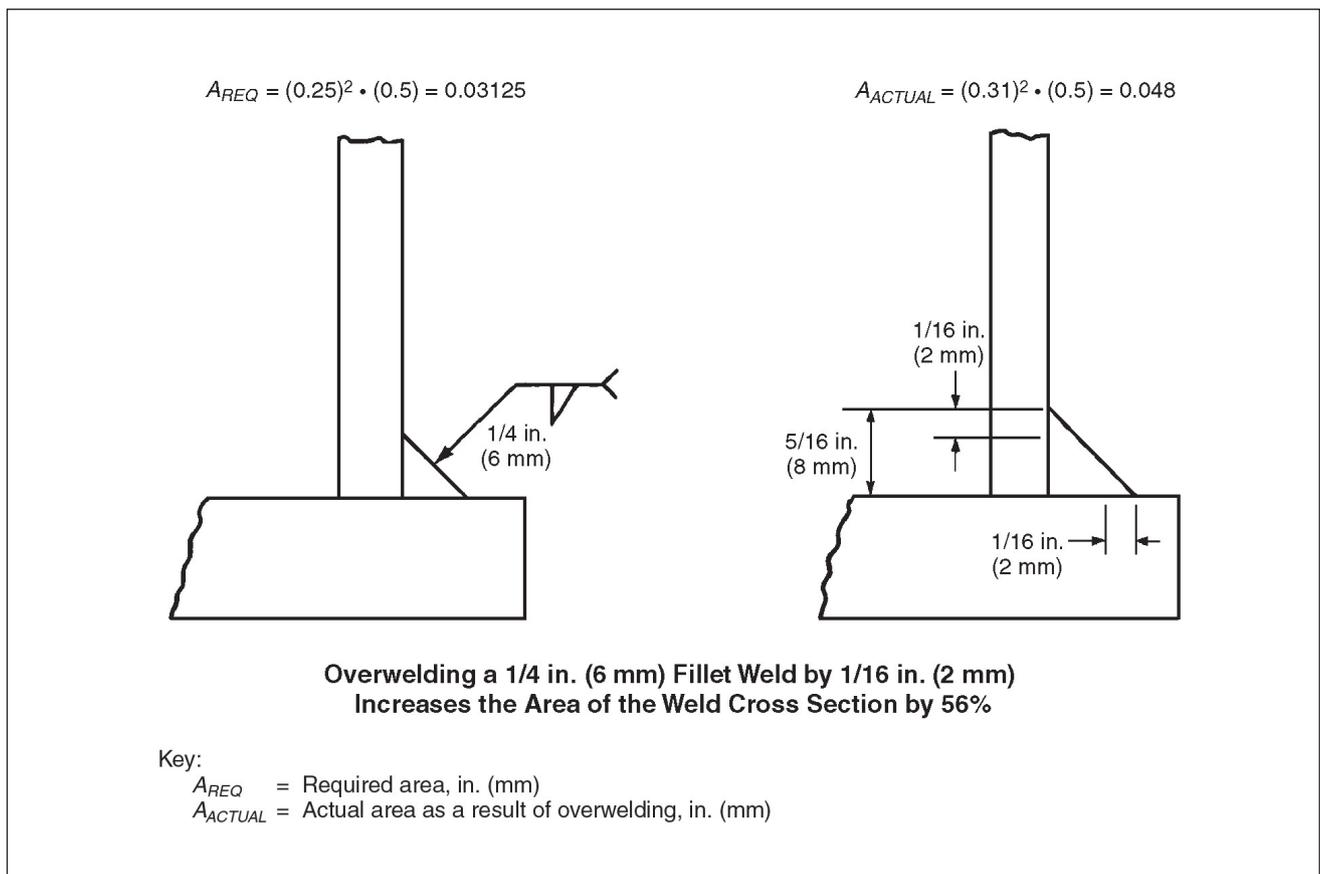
Efecto de la sobre soldadura en una sección transversal de soldadura.
